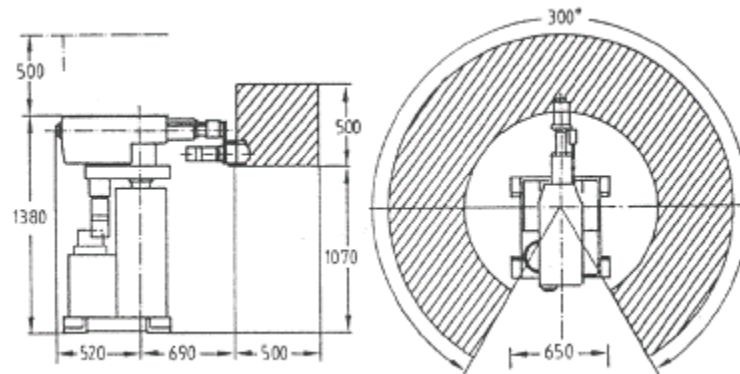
Robot seriale a geometria cilindrica: vista laterale e vista in pianta
